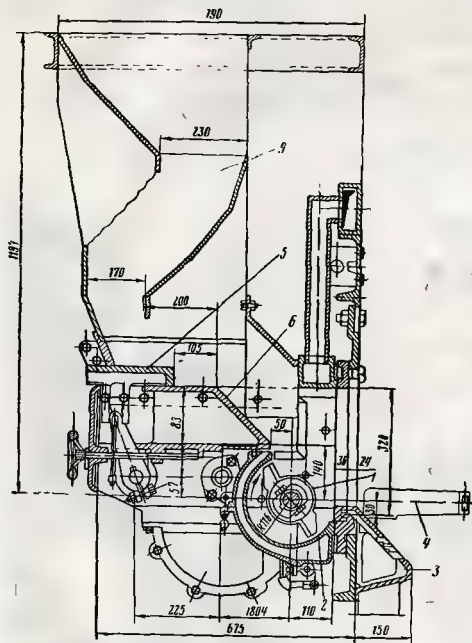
Пневмомеханический забрасыватель топлива типа ПМЗ конструкции ЦКТИ: 1 — ротор; 2 — цилиндрический лоток; 3 — воздушная фура; 4 — боковые воздушные сопла; 5 — плунжер; 6 — разгонная плита; 7 — редуктор; 8 — кулисный механизм; 9 — каскадно-лотковый угольный бункер
